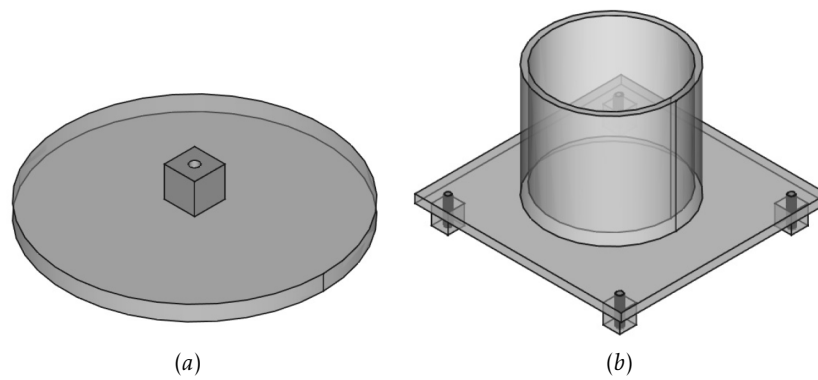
Vista isométrica del diseño CAD: (a) tapa rotatoria y (b) base con el cilindro.
